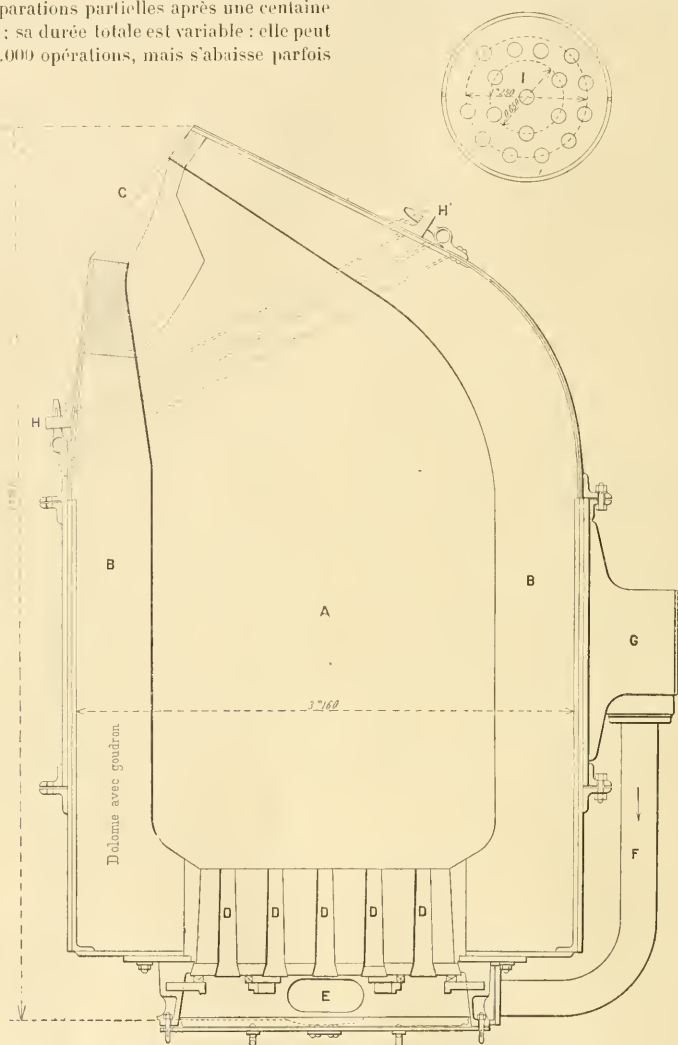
Convertisseur Bessemer.* — A, cornue; B, garnissage en pisé; C, gueulard; D, tuyères; E, boîte à vent; F, conduite de vent; G, ceinture; H H', clavettes d'assemblage; — I, coupe du fond.
